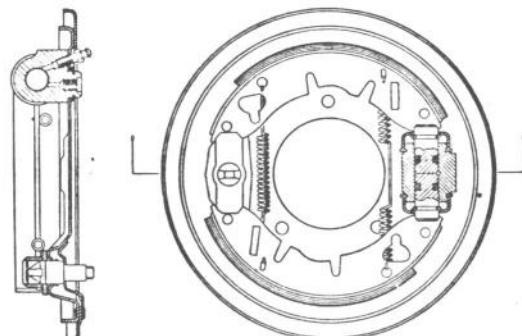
Mecanismo de freno delantero de tambor, de una zapata principal y un sólo cilindro receptor.
